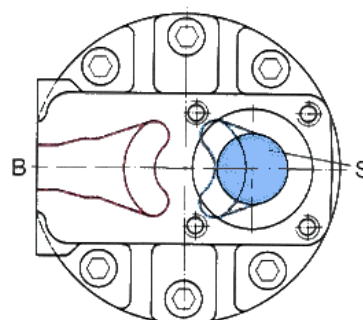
Bomba de pistones axiales con eje de motor inclinado.
